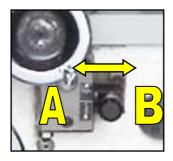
Avanzamento trasversale → A / Avanzamento longitudinale → B.
